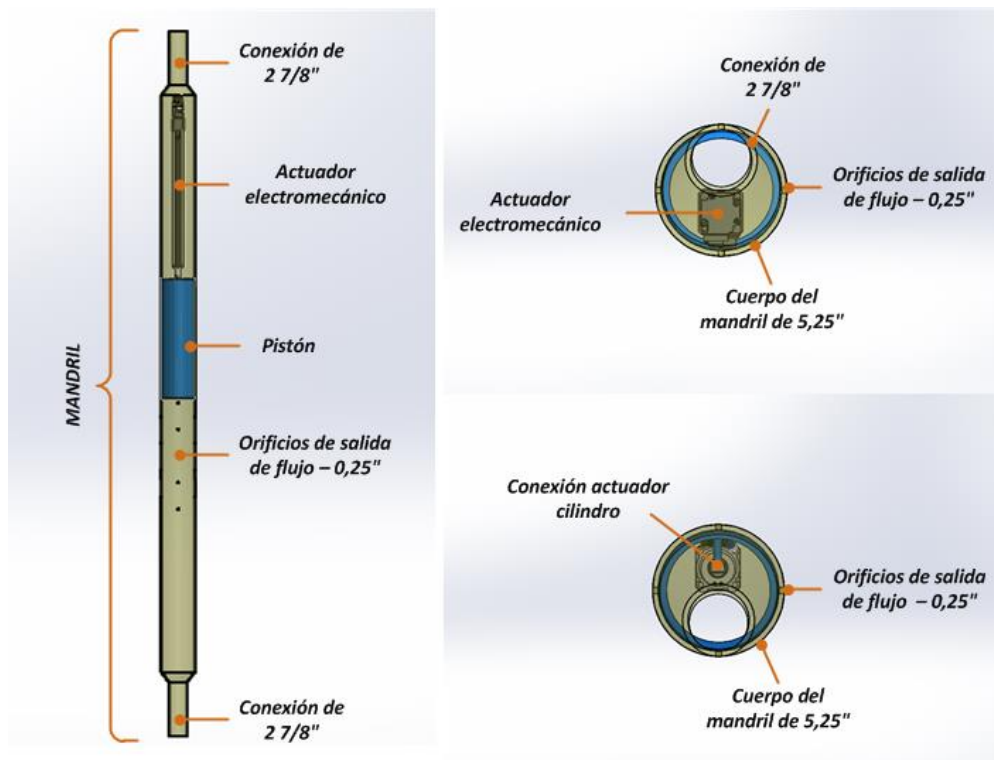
Descripción del primer diseño realizado: placa cilíndrica deslizante con actuador electromecánico. Fuente propia.
